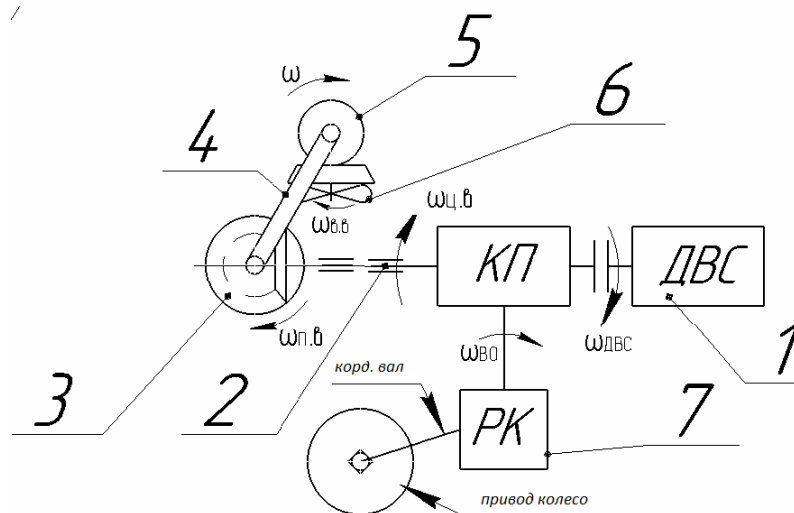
Кинематическая схема ТС на ВП с опорными колесами:
